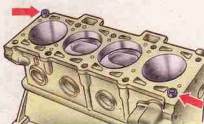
Втулки для центрирования головки на блоке цилиндров
